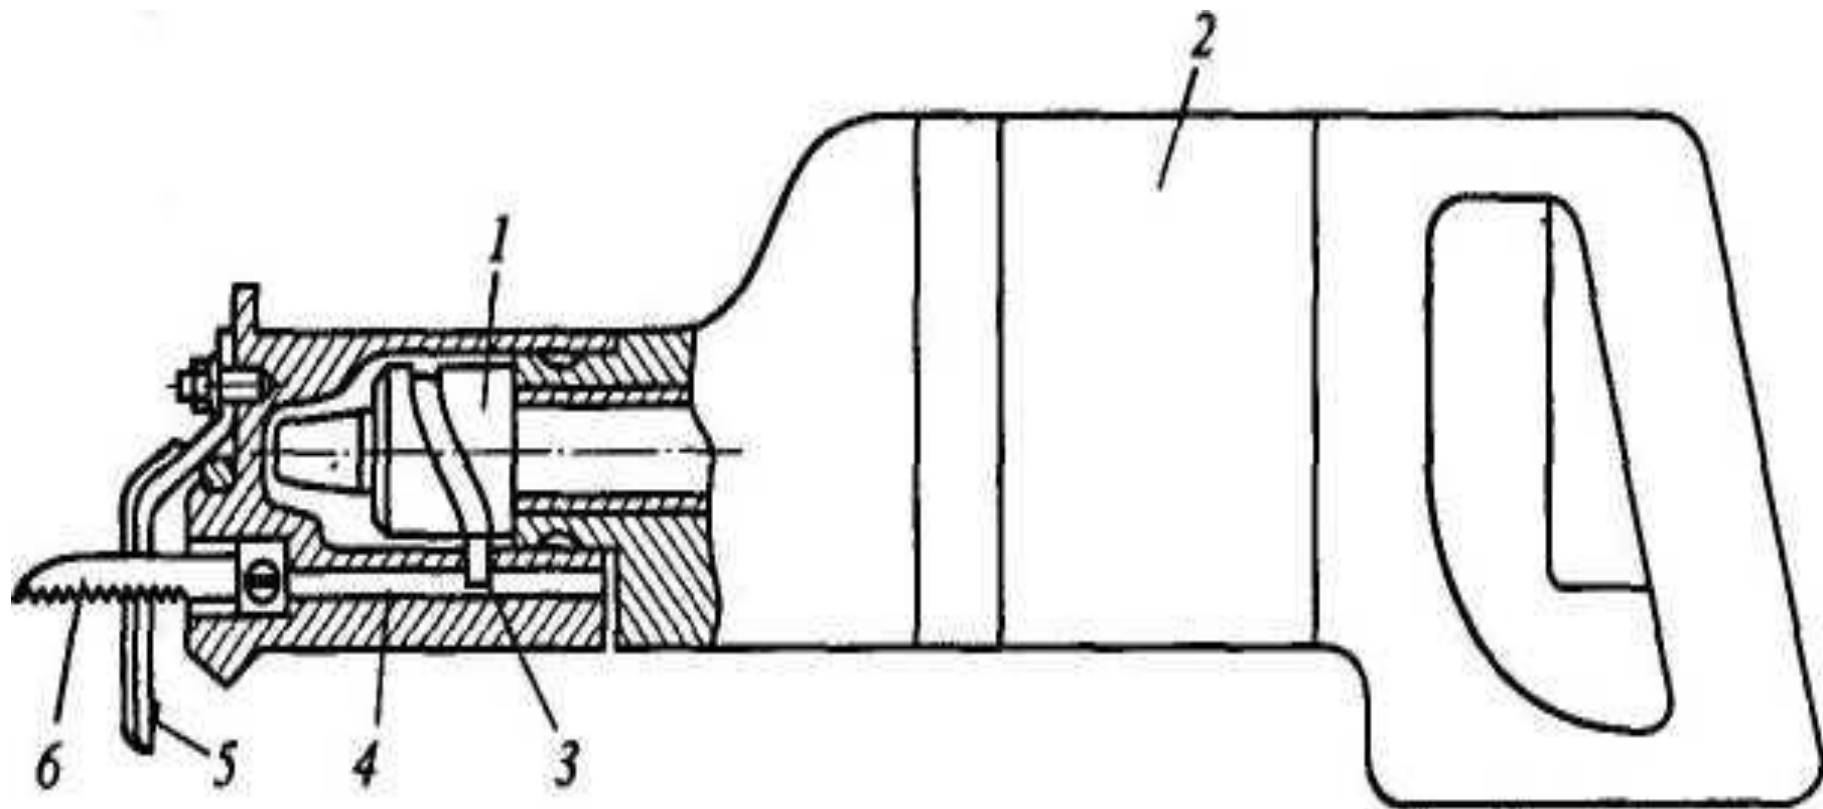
Механическая ножовка: 1 - барабан; 2 - корпус; 3 - палец; 4 - ползун; 5 - скоба; 6 - ножовочное полотно
